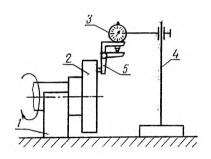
Схема проверки биения торца фланца коленчатого вала: 1— призма; 2— фланец коленчатого вала; 3— индикатор; 4— универсальный штатив; 5— угловой рычаг.
